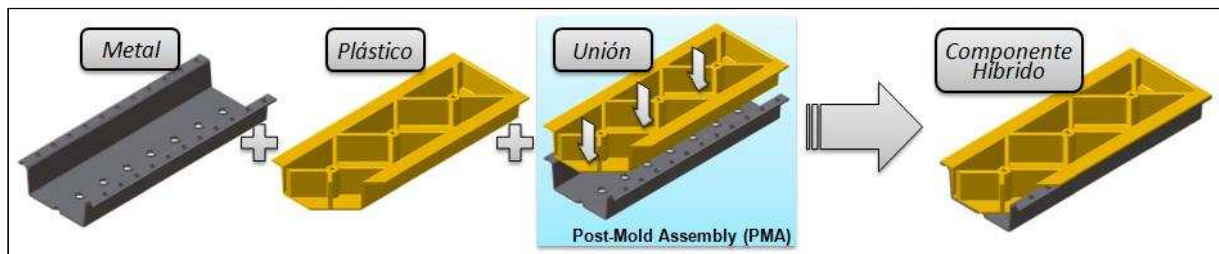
PROCESO PRODUCTIVO DE UNIÓN IN-MOLD ASSEMBLY. PMA
